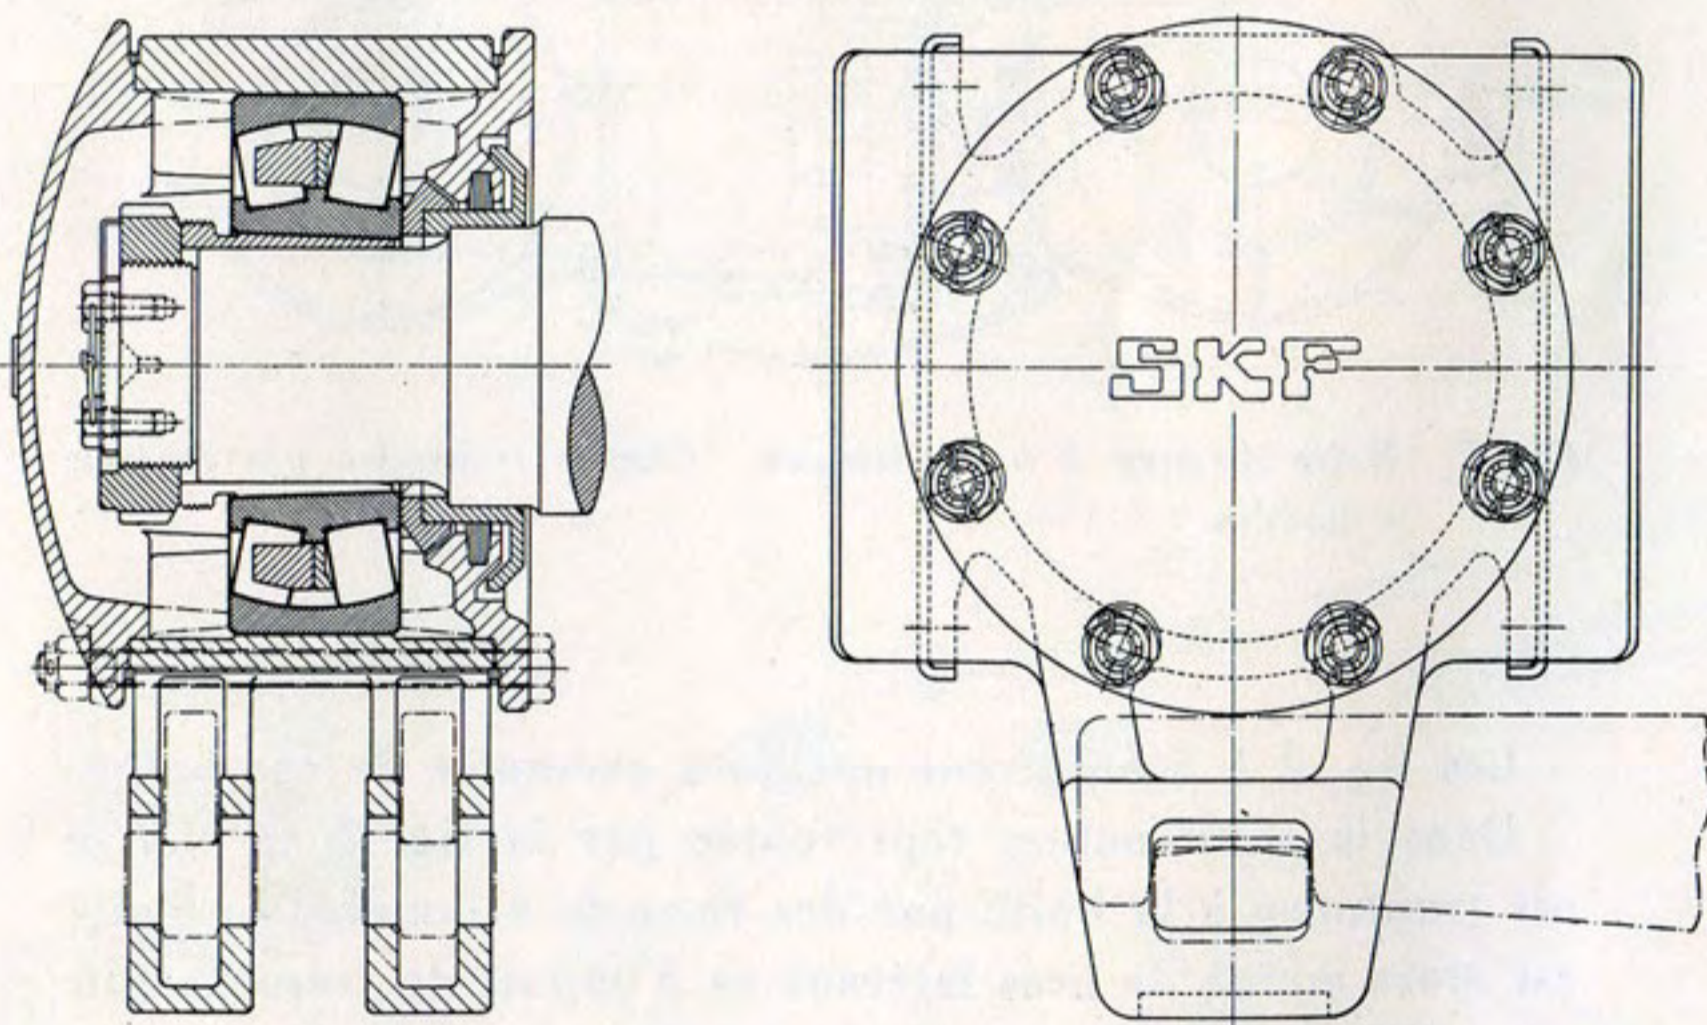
Boîte d'essieu SKF à un roulement à rotule sur rouleaux et manchon de démontage.
